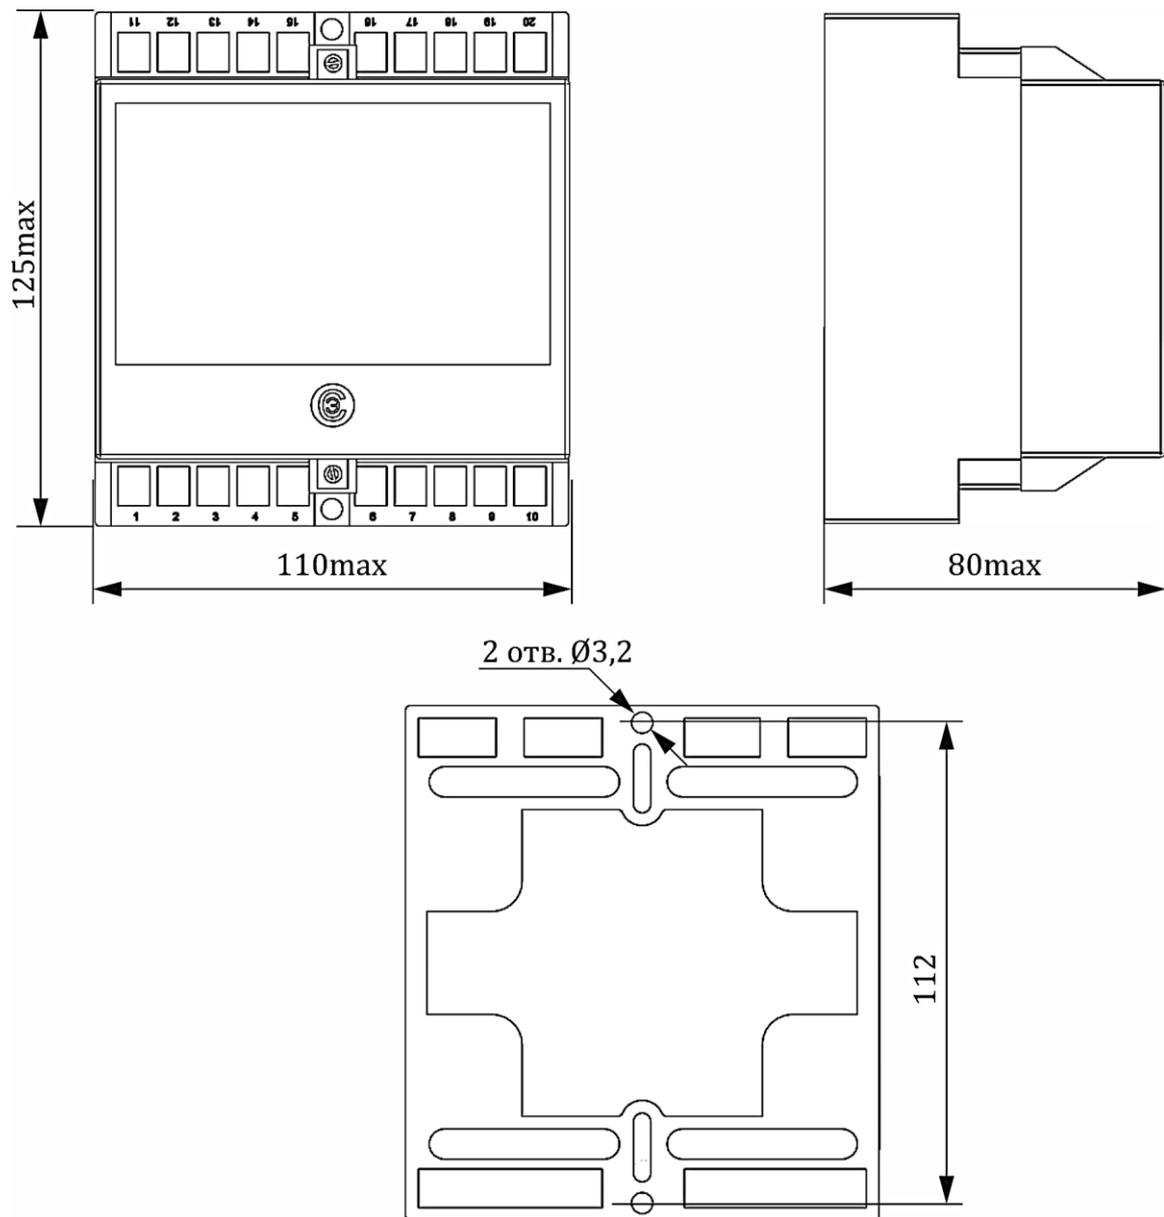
Габаритные и установочные размеры корпуса E20
